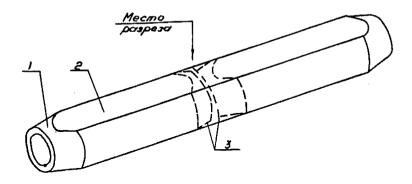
Разрезение корпуса стандартного соединательного зажима пополам:
